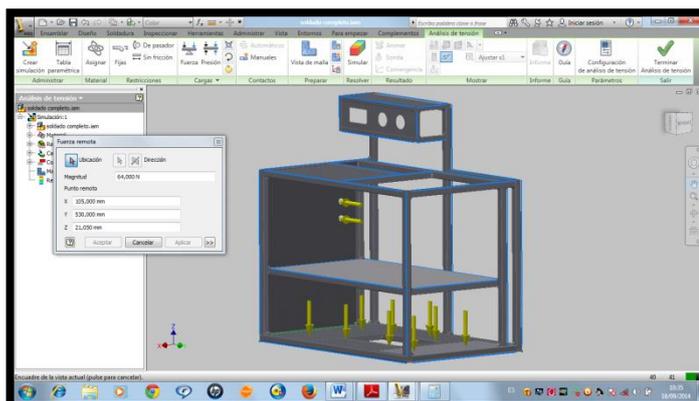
7. Fuerza aplicada en puntos de la estructura inferior
